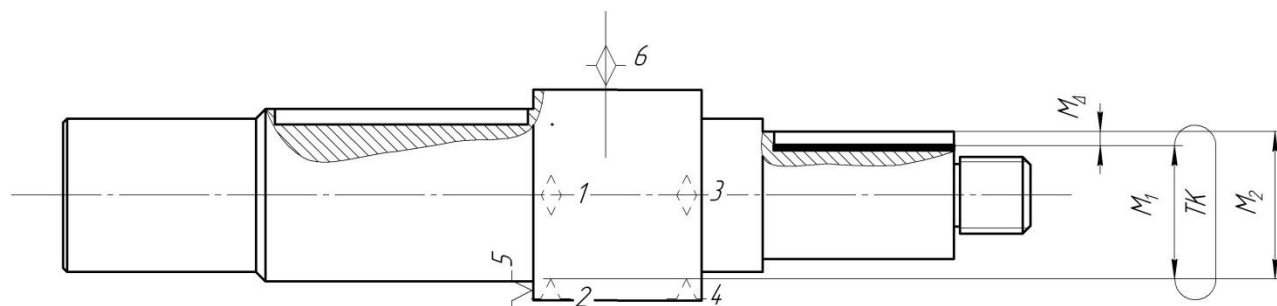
Базування вала (другий варіант) при обробці шпонкового валу
